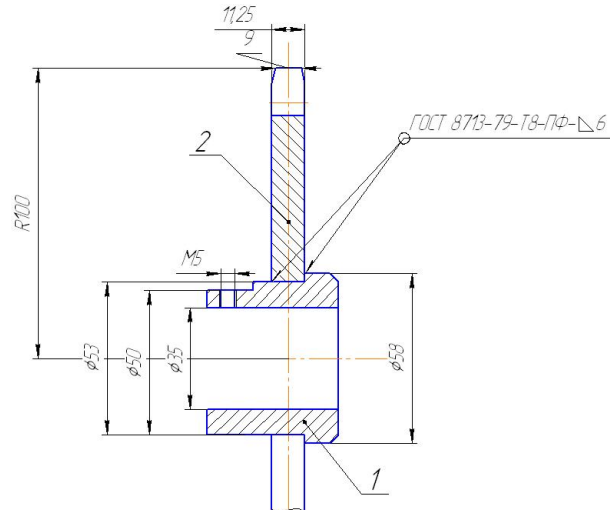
Зірочка приводу транспортера: 1 – корпус; 2 – зірочка.
